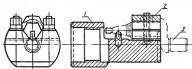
Приспособление для обтачивания кривошинной шейки вала автомобильного компрессора: 1 — коопус: 2 — новища: 3 — облабатываемая деталь.
